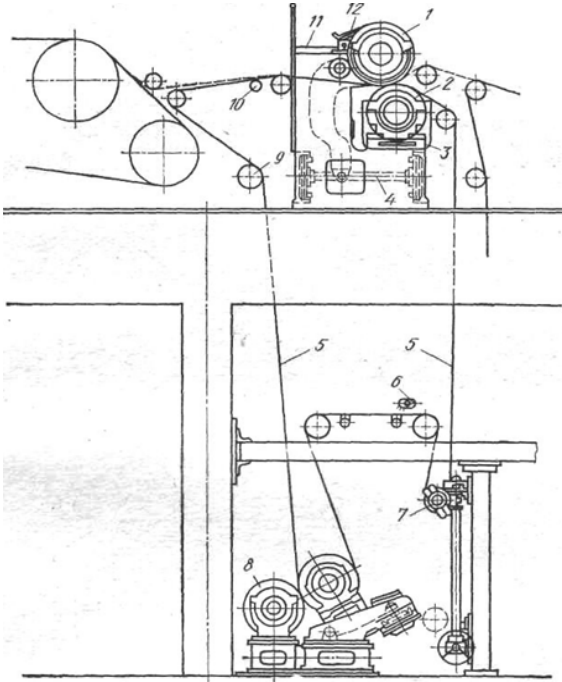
Двовальний прес: 1 - верхній гранітний вал; 2 - нижній вал; 3 - корито для збору води; 4 - механізм притиску валів; 5 -сукно; 6 - водяний сприск; 7 - сукнонатяжний валик; 8 - вальцьова сукномийка; 9 - сукноправильний валик; 10 - відсмоктувальний ящик; 11 - перехідний місток; 12 – шабер.
